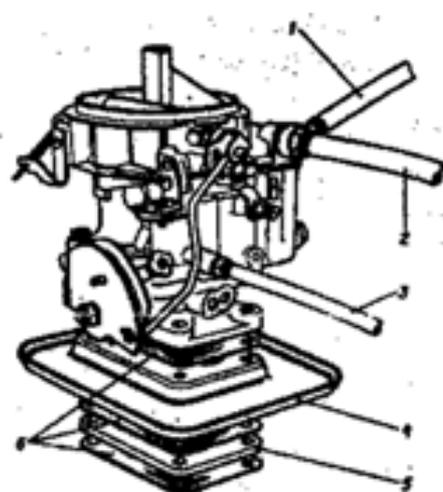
Топливопроводы карбюратора К-126Л: 1 - трубка рециркуляции топлива; 2 - трубка подачи топлива в карбюратор; 3 - трубка к вакуумному корректору; 4 - топливоборник; 5 - проставка; 6 - прокладка паронитовая
